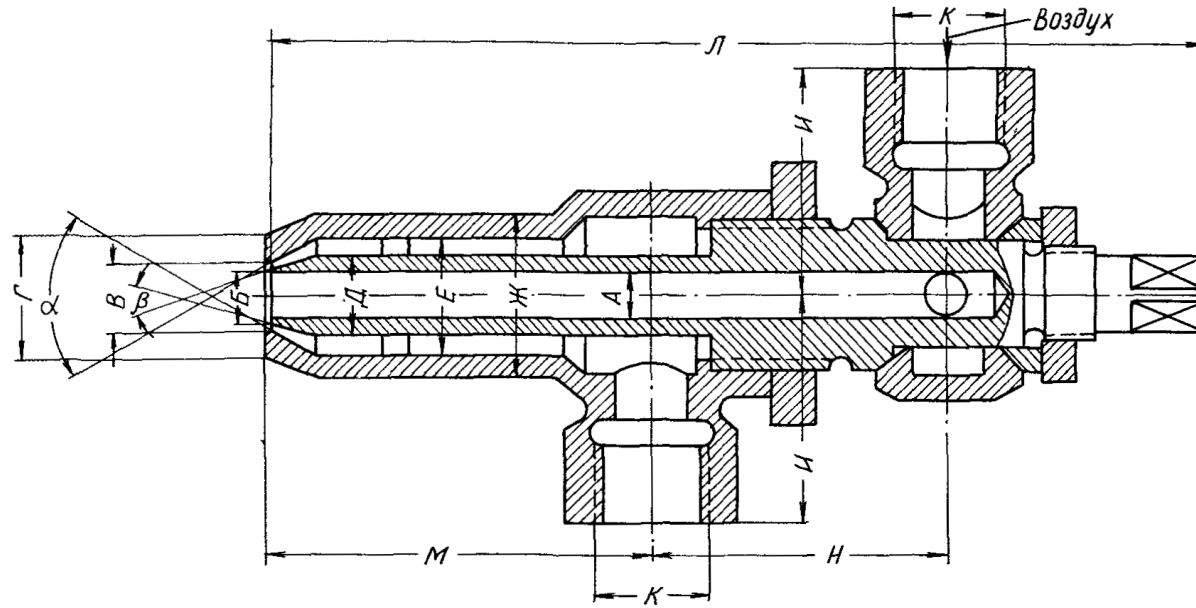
Форсунка высокого давления конструкции Шухова [6]
